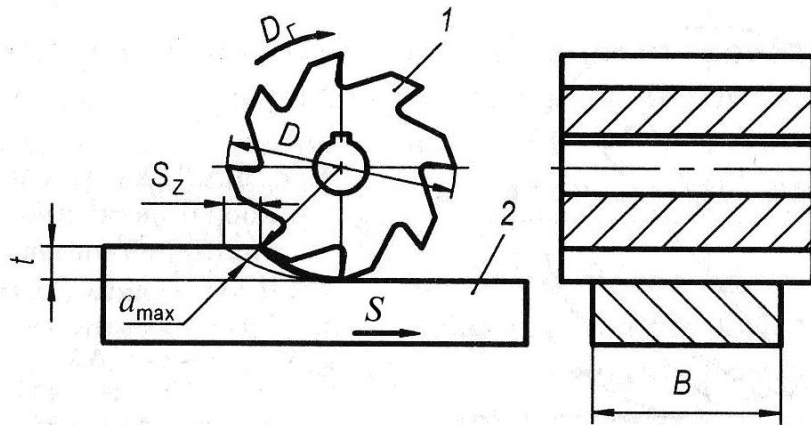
Елементи режиму різання при фрезеруванні:
